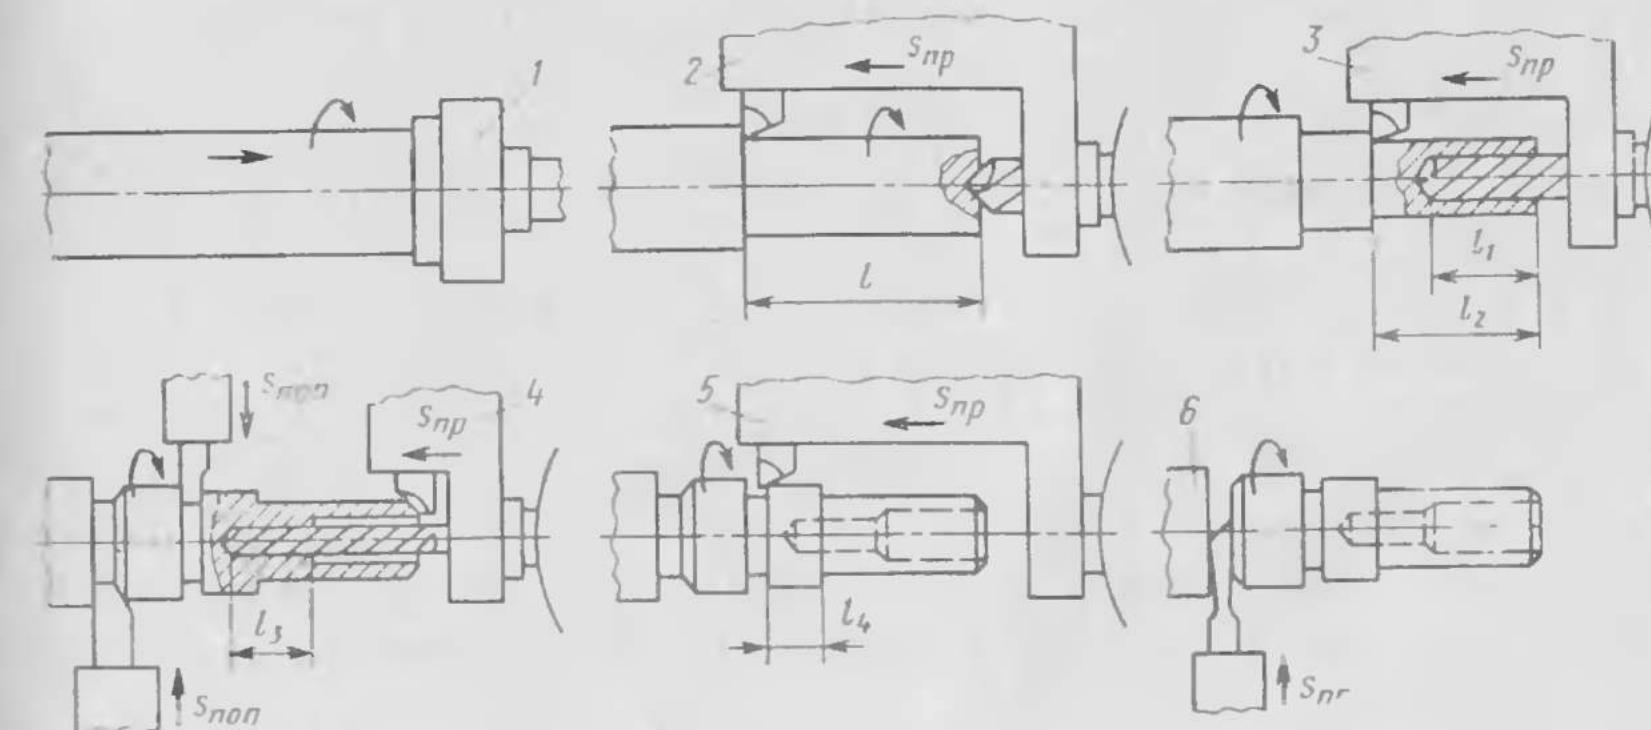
Схема обработки типовой детали на токарно-револьверном автомате:
